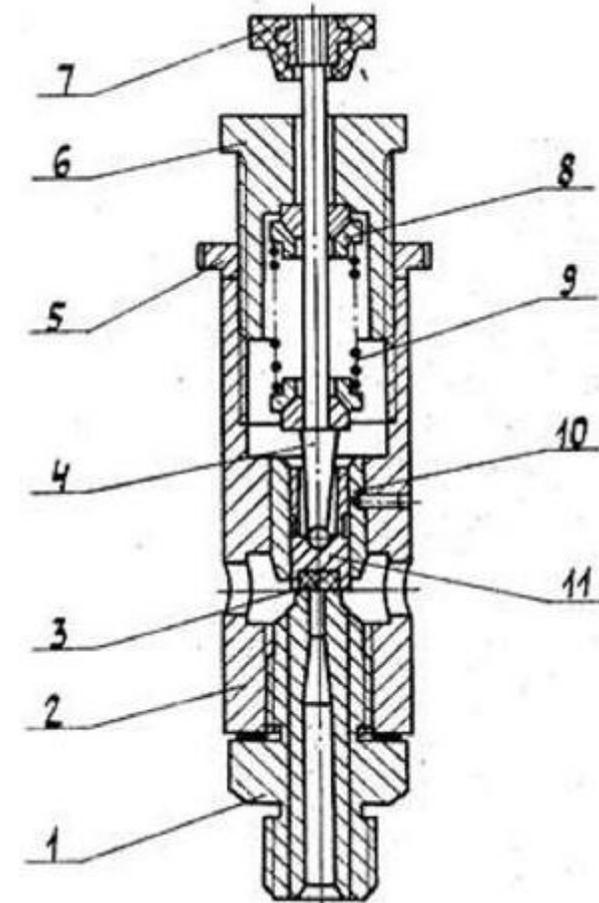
Клапан предохранительный установки компрессорной ВК-57М1.
